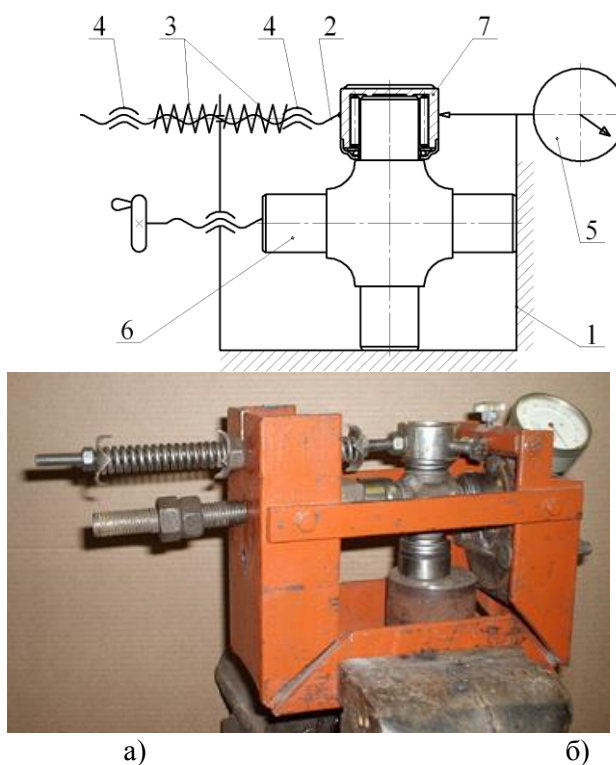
Приспособление для измерения радиального зазора в подшипниковых узлах карданных шарниров:
